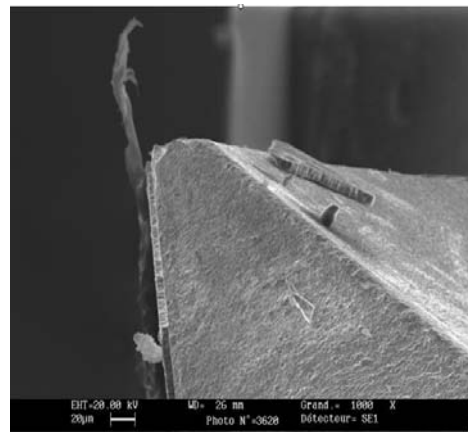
casse de la fraise 3 après 7m d'usinage
